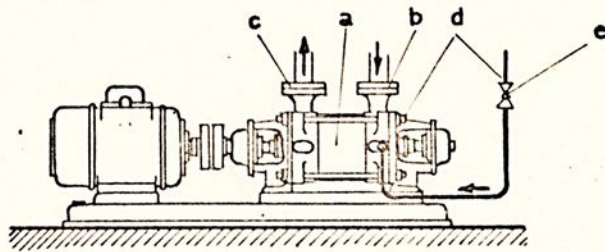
BOMBA A VÁCUO OU COMPRESSOR COM REFRI-
